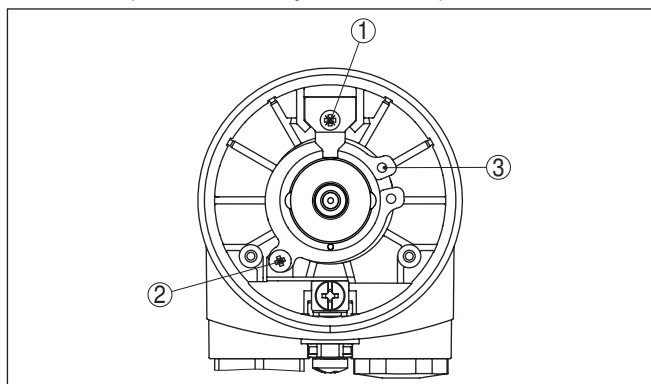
Положение винтов и стопорного кольца, например, на пластиковом корпусе
